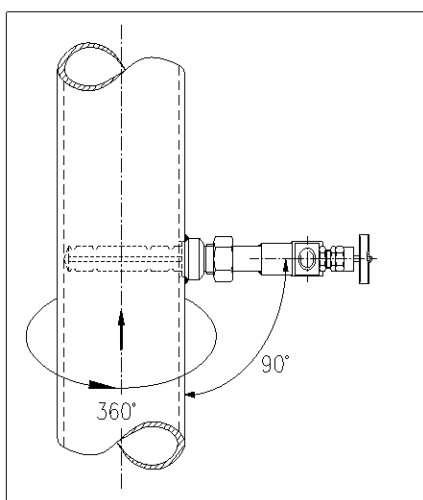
Installation sur conduite verticale pour liquides ou gaz
